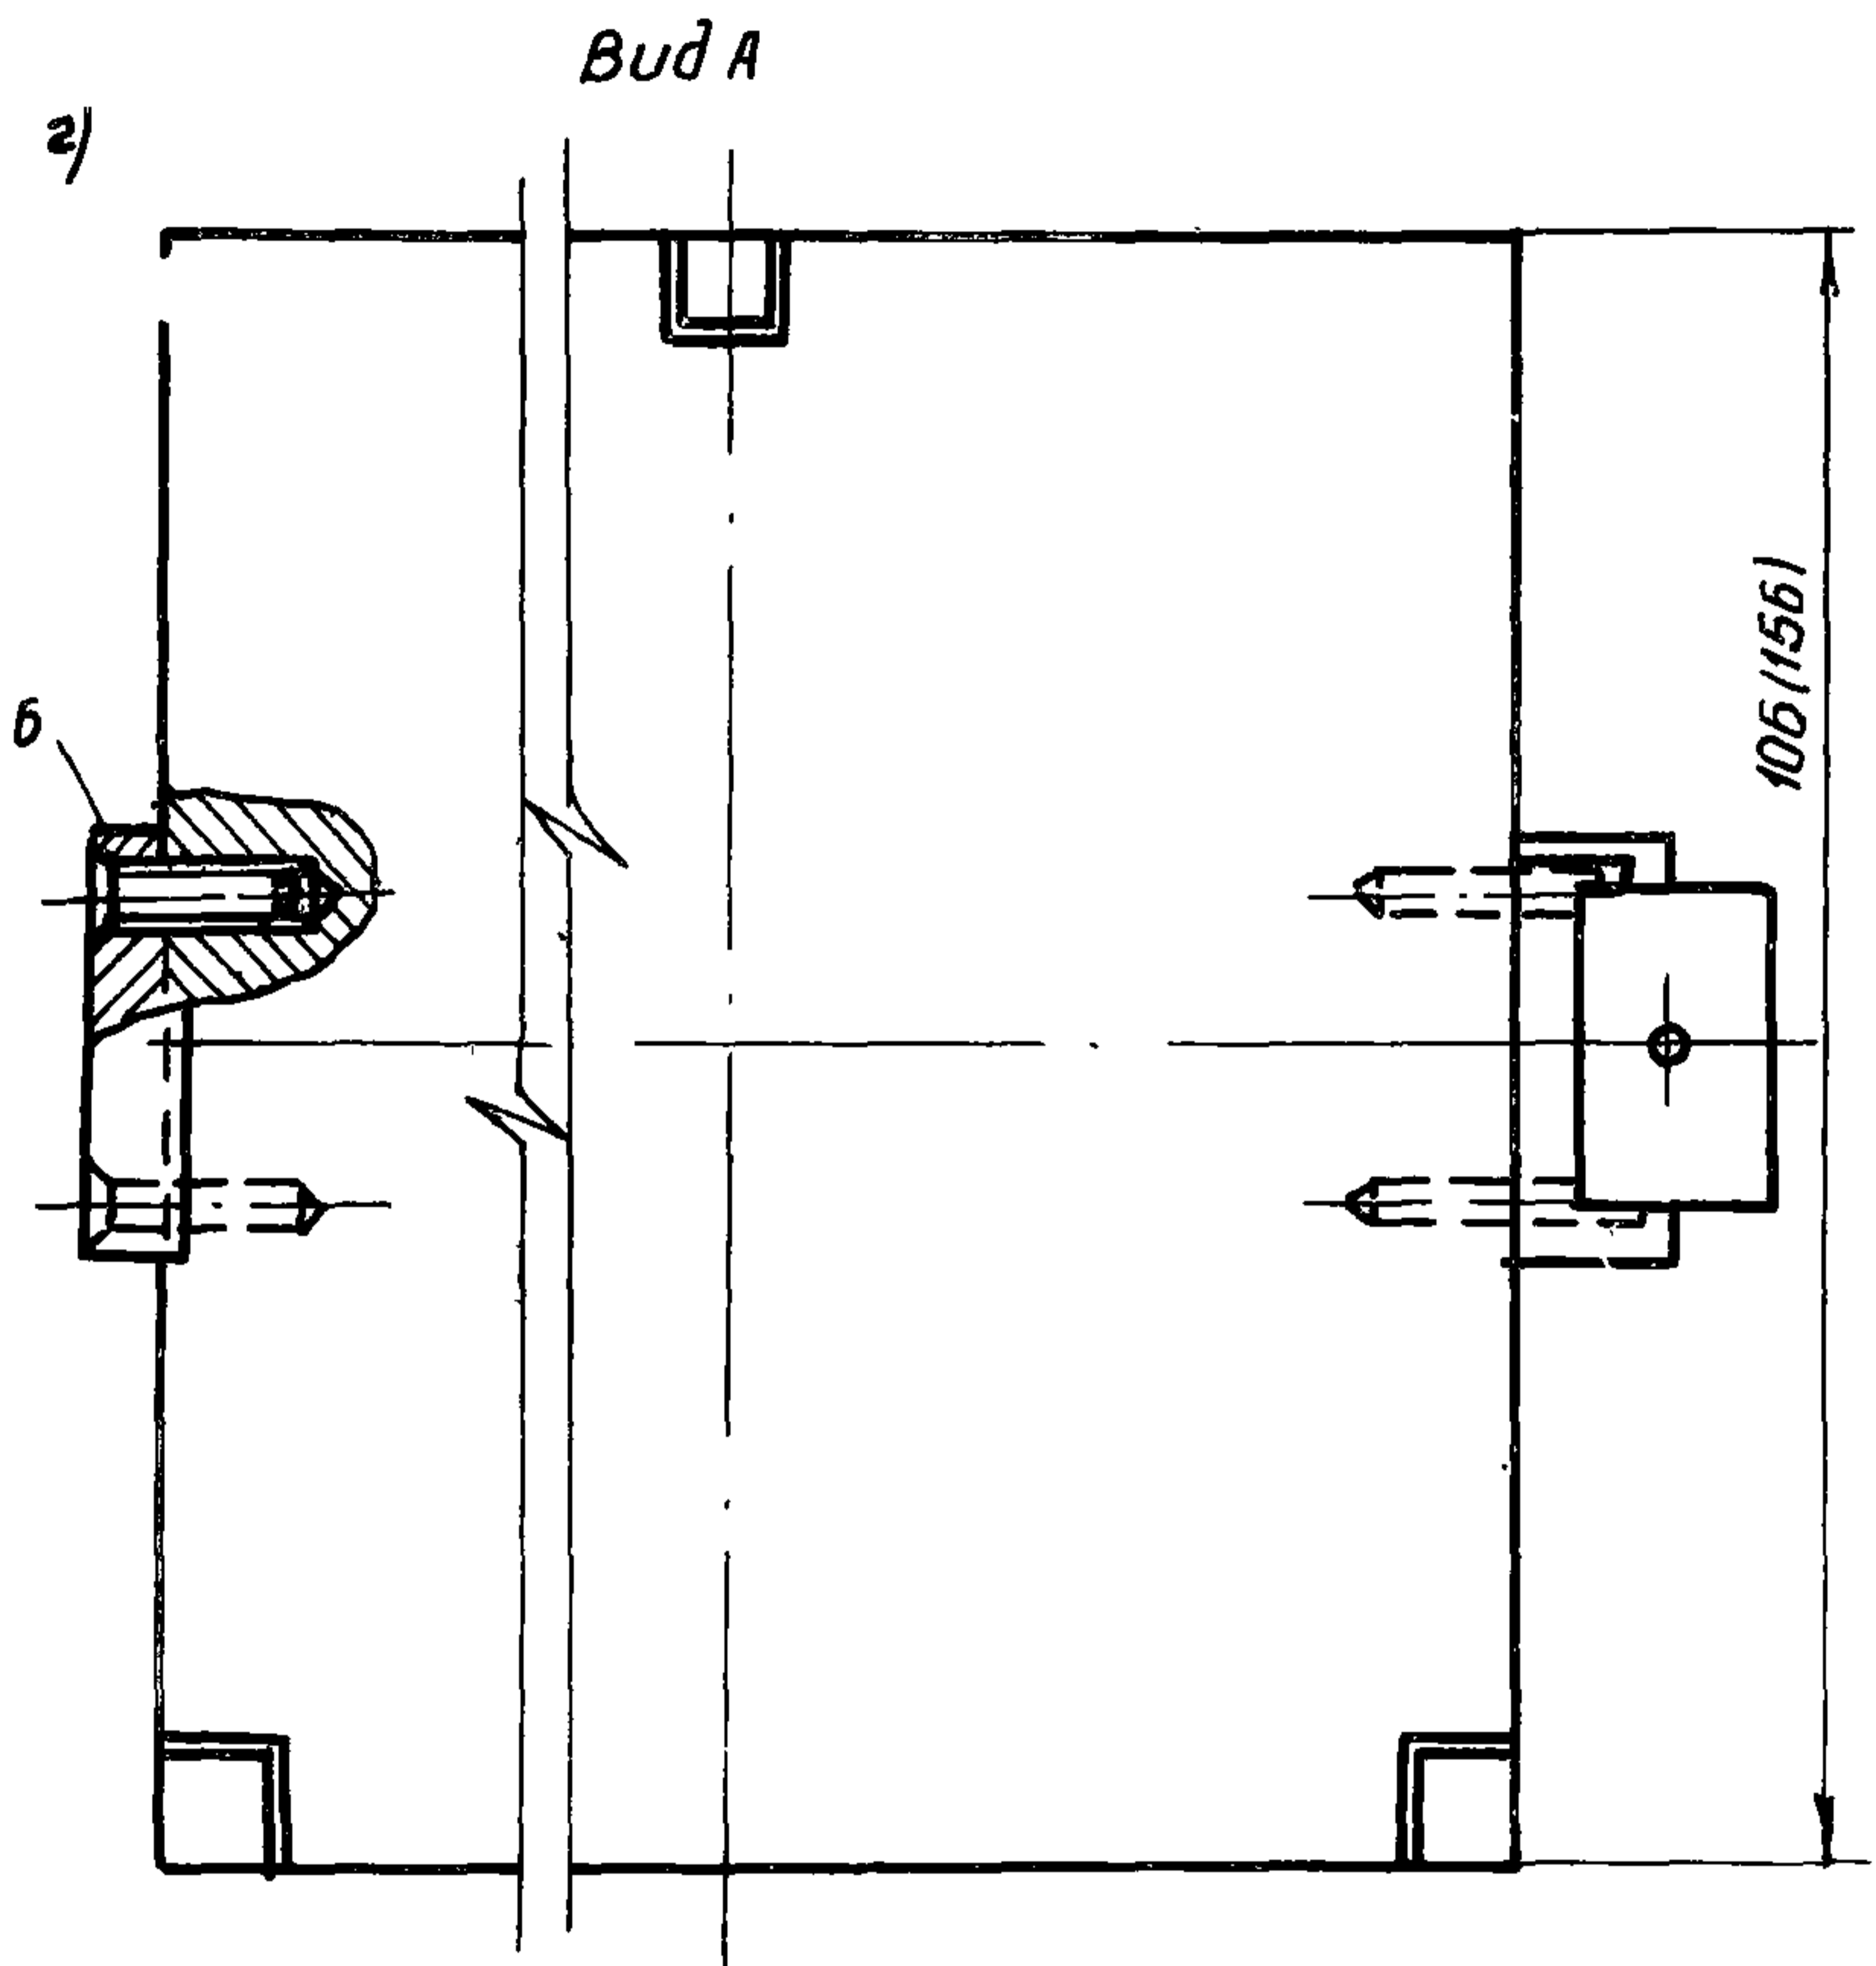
, г. Общий вид прибора. Подставка (вид А)
